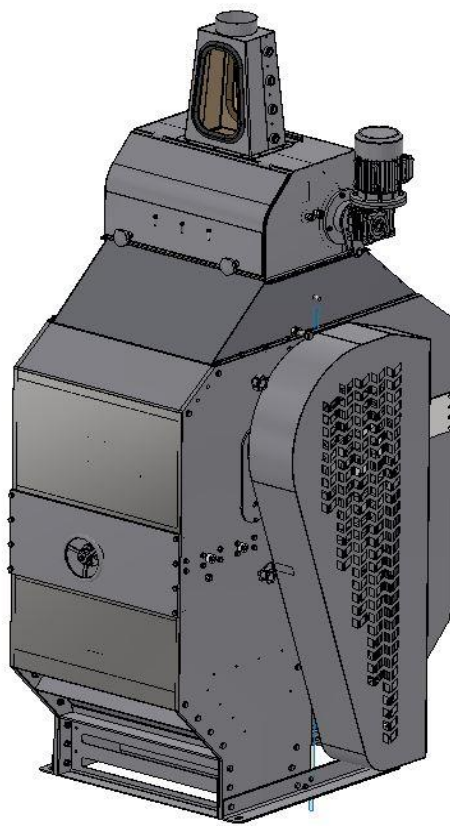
Загальний вид модернізованого вальцедекового верстата
